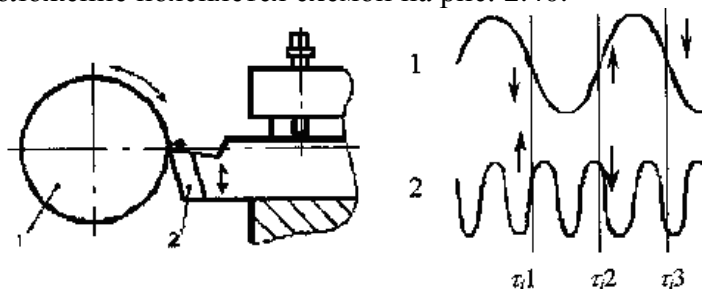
Схема колебательных движений заготовки 1 и режущего инструмента 2 в процессе резания.
